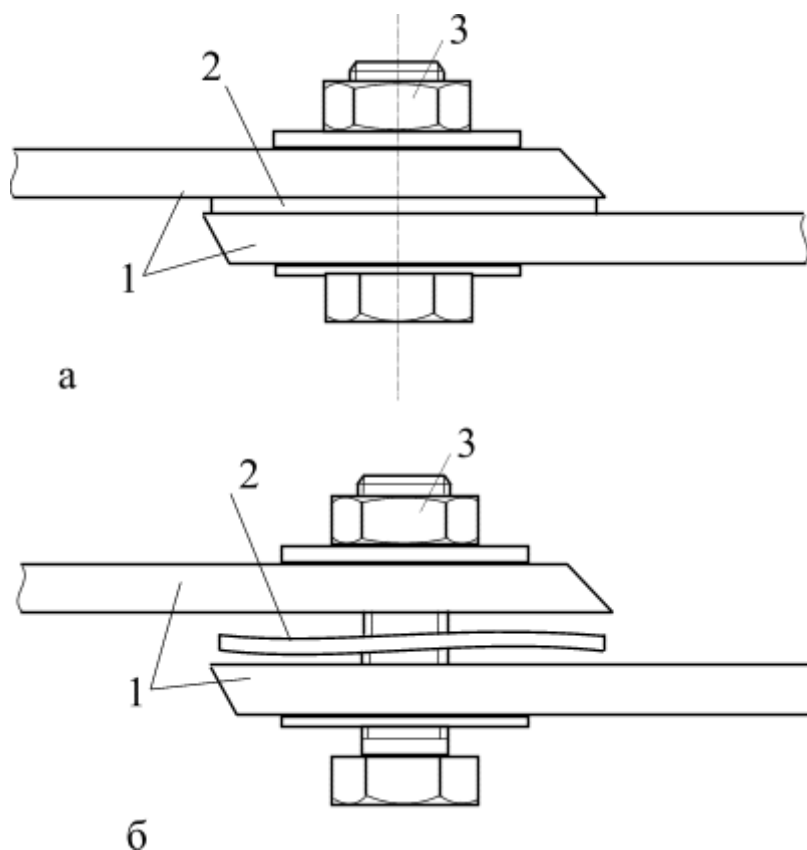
Загальний вигляд розбірного контактної вузла з використанням пластини із сплаву з ефектом пам'яті форми
